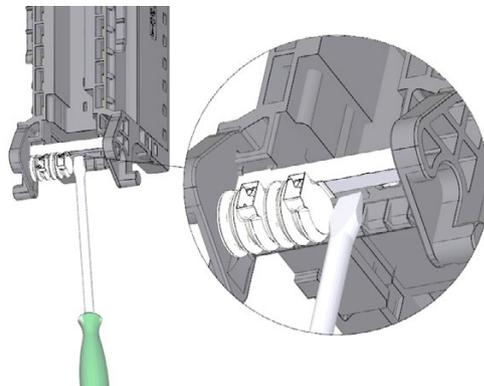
Desmontaje del elemento codificador mecánico del conector frontal
